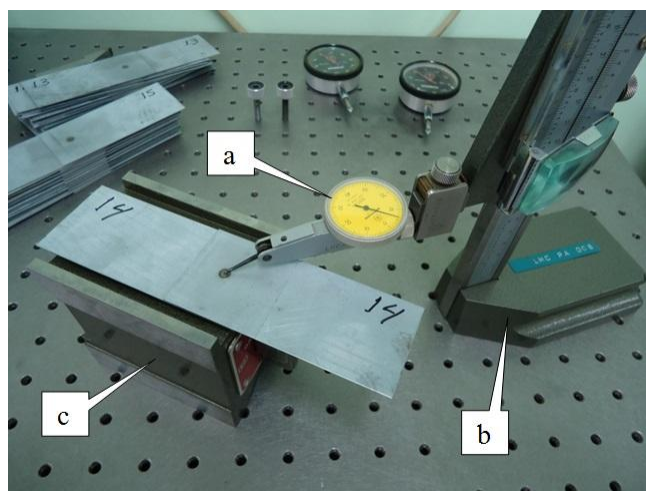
Medição da indentação da solda.(a) Relógio apalpador, (b) Traçador de altura, (c) Bloco magnético.
